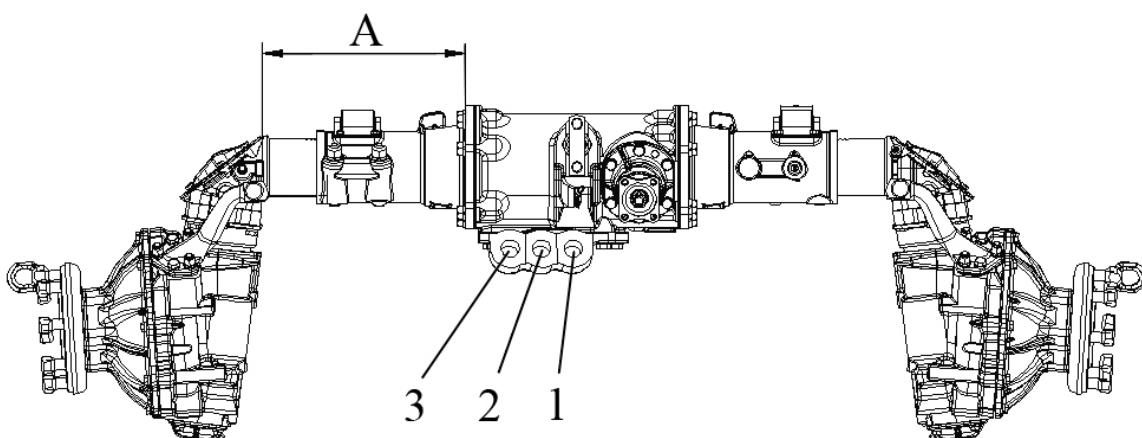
Схема изменения колеи передних колес трактора с установленным ПВМ 72-2300020-А-04
